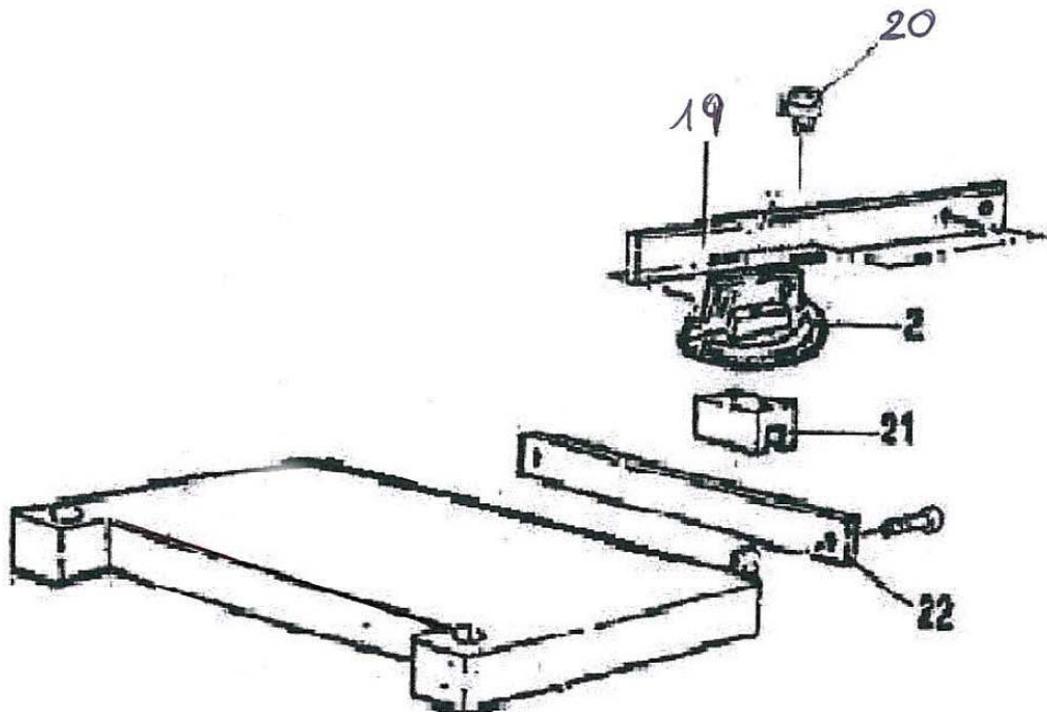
Ersatzteilzeichnung 3 Langlochbohrmaschine LLB 30
